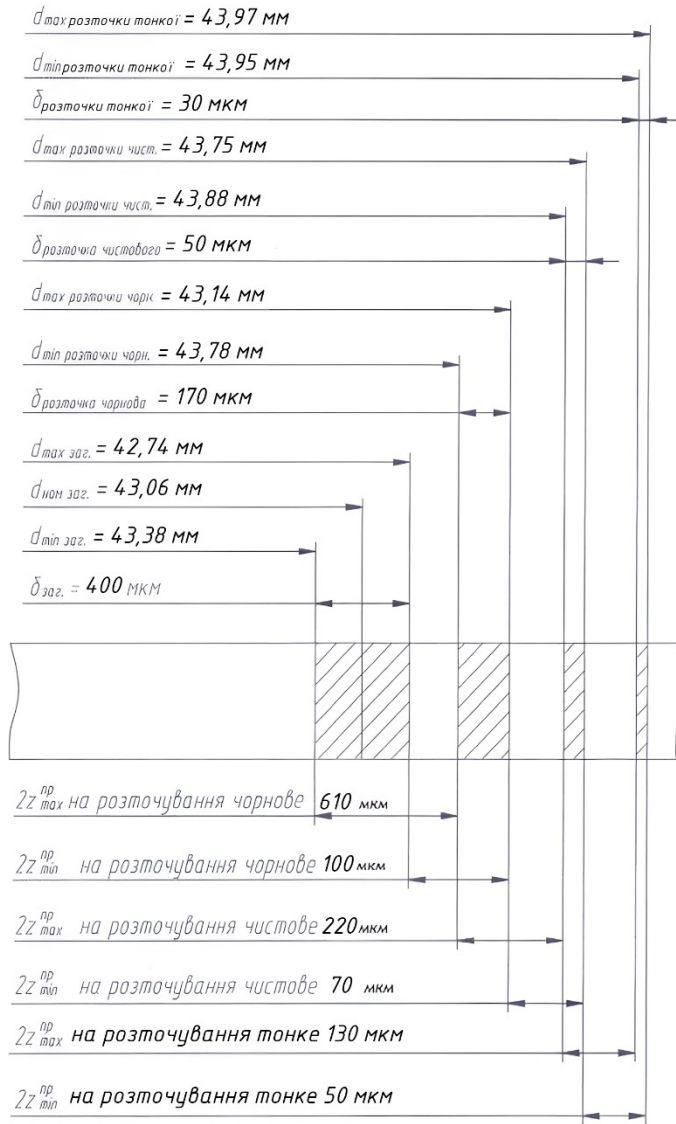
Схема розташування полів припусків і допусків на обробку поверхні  $\varnothing 44 \text{ H6}$
